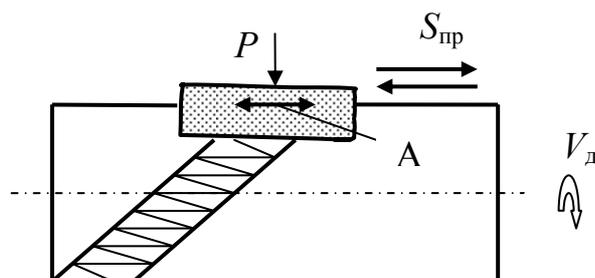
Схема суперфиниширования цилиндрической поверхности
